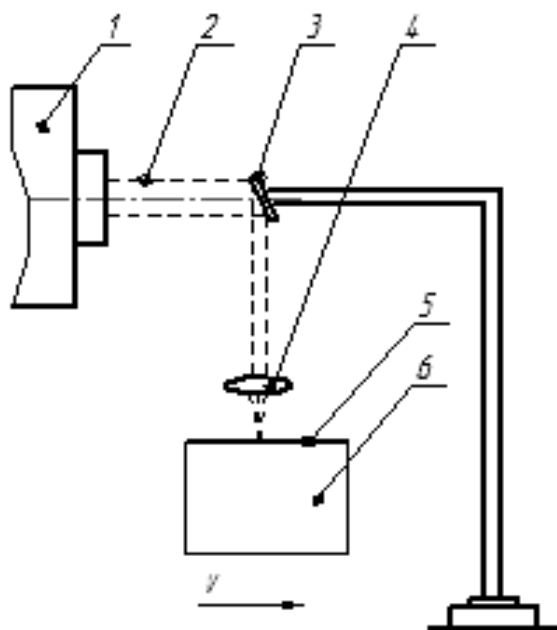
Схема лазерной установки: 1 – разрядная трубка; 2 – лазерный луч; 3 – поворотная оптика; 4 – фокусирующая оптика; 5 – упрочненная поверхность; 6 – деталь
